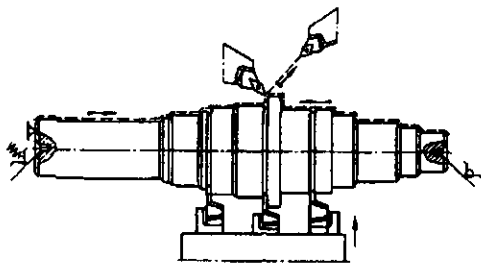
Наладка полуавтомата с двумя копирвальными суппортами для обработки ступенчатого вала
